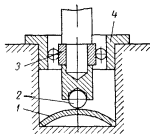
Схема опоры с принудительным движением в направлении оси цапфы
